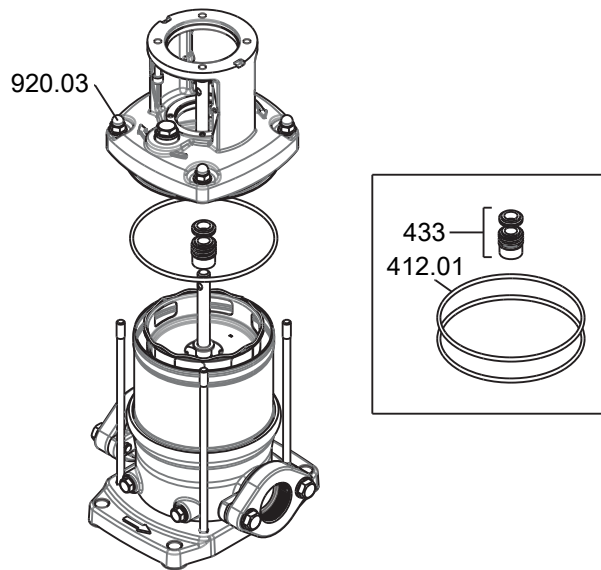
Desmontaje de la escuadra de apoyo 89-11.03
